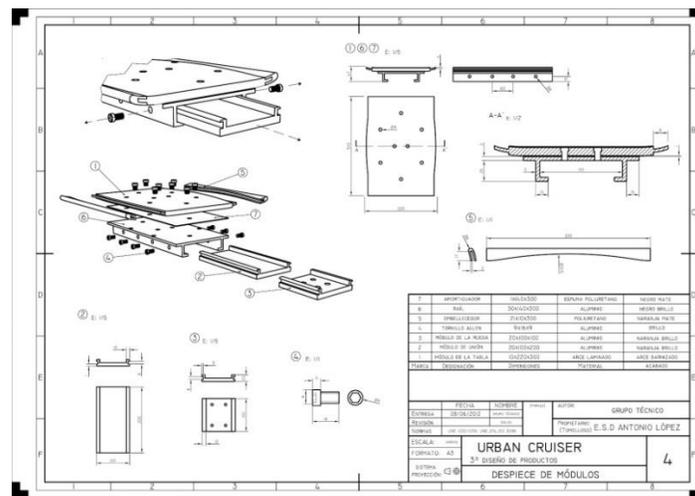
Ejemplo Planos de Construcción. (Sandro Proyectos)
